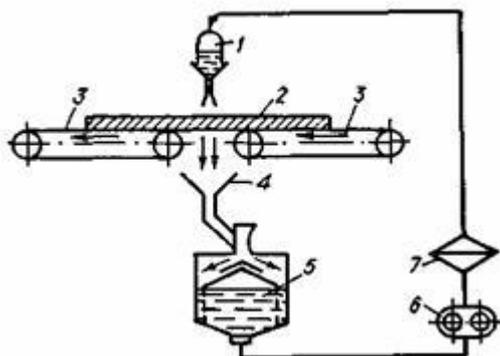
схема работы лаконаливной машины: 1 - наливочная головка; 2 - покрываемое изделие; 3 - транспортирующие устройства; 4 - приемный лоток; 5 - отстойный бак; 6 - насос; 7 - фильтр
